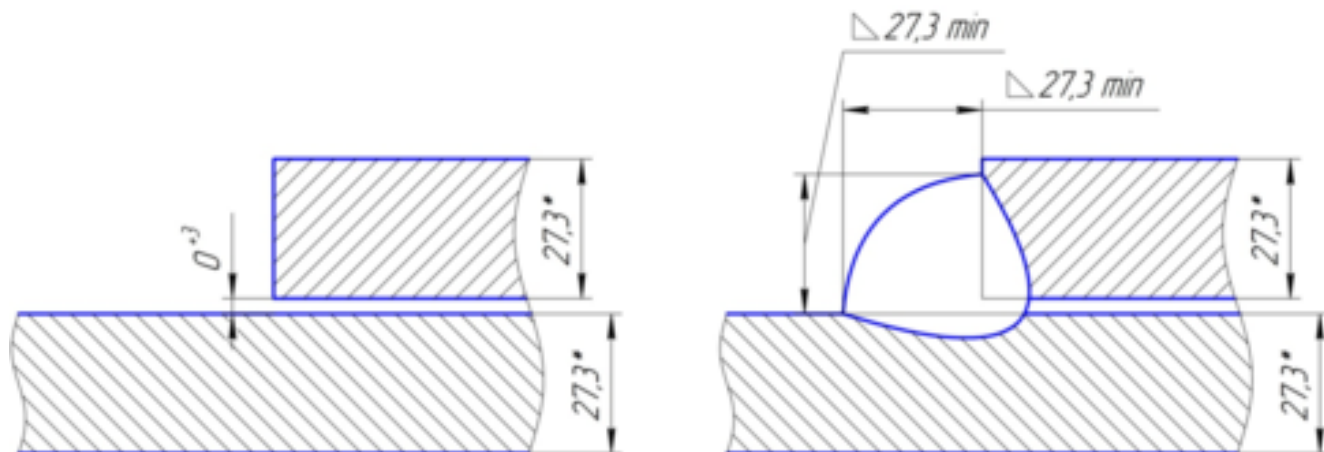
Общий вид сварного шва №2
